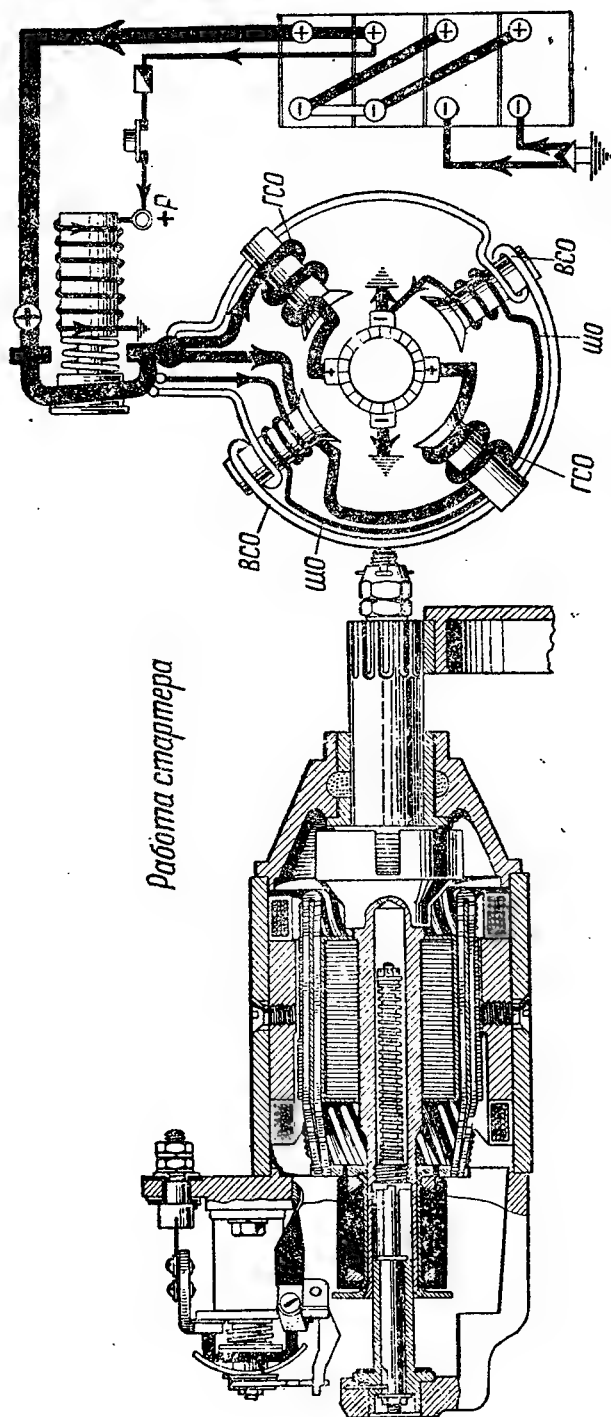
Стартер СМТ (положение деталей стартера и путь тока при запуске двигателя)
